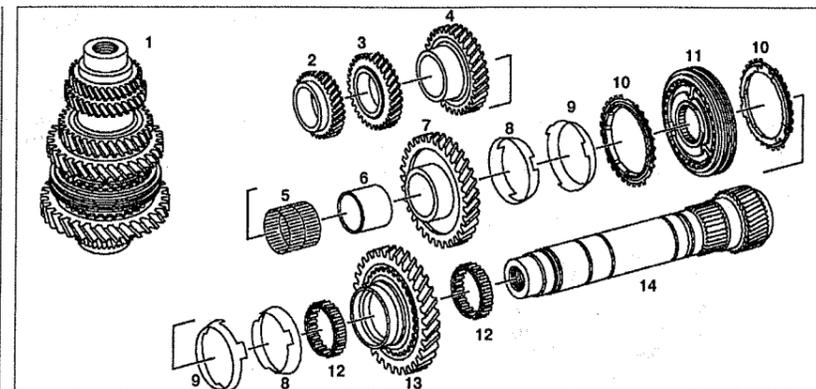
Ведомый вал (автомобили с двигателем 611.980):
